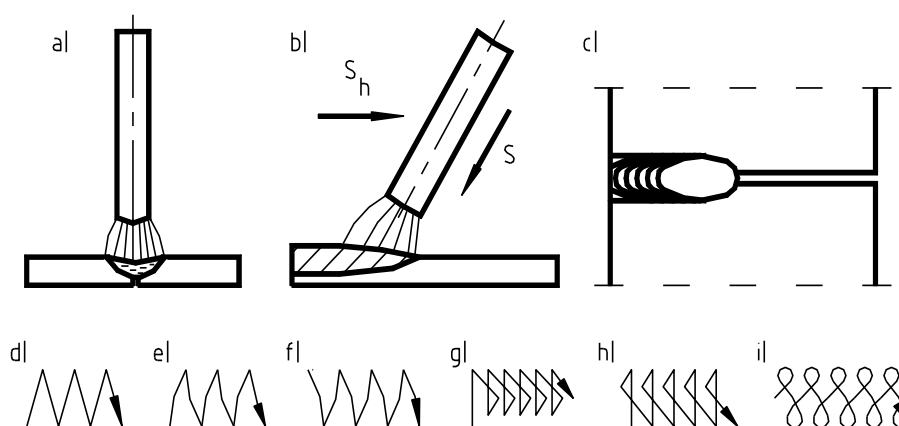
Esquema de soldadura pelo arco voltaico.
